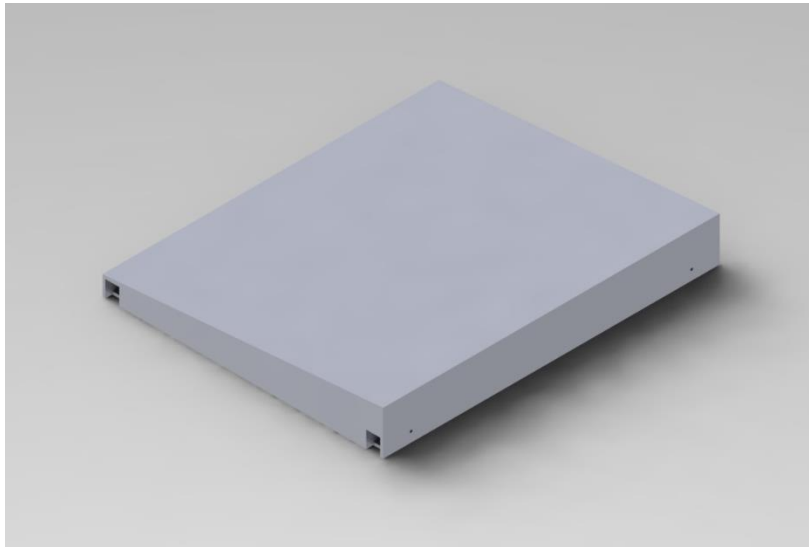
Ensamblaje subconjunto 1.4. Soldadura 45, 46, 47 y 48.
